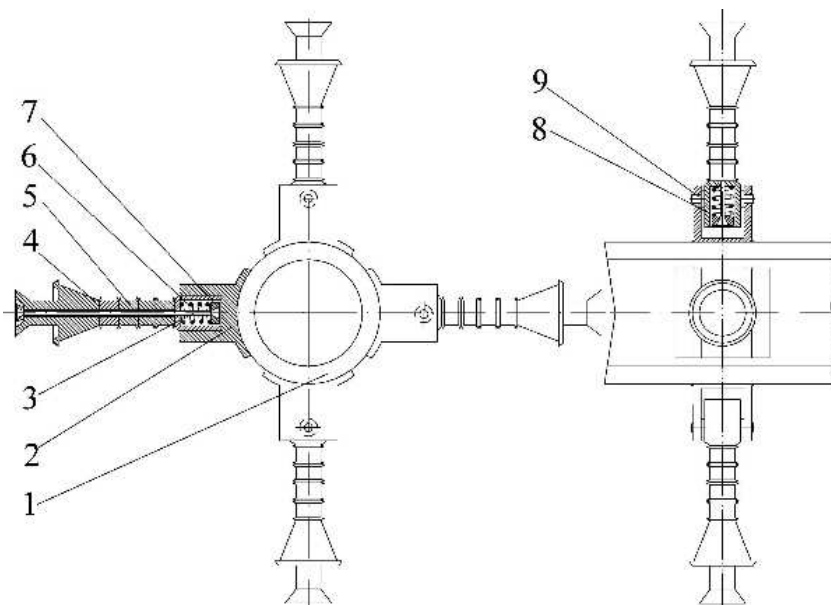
Рабочий орган разработанной машины: 1 – горизонтальный вал; 2 – кронштейн; 3 – гибкая связь; 4 – комбинированный нож; 5 – втулка; 6 – пружина; 7 – упорная концевая шайба; 8 – стакан; 9 – полуось
